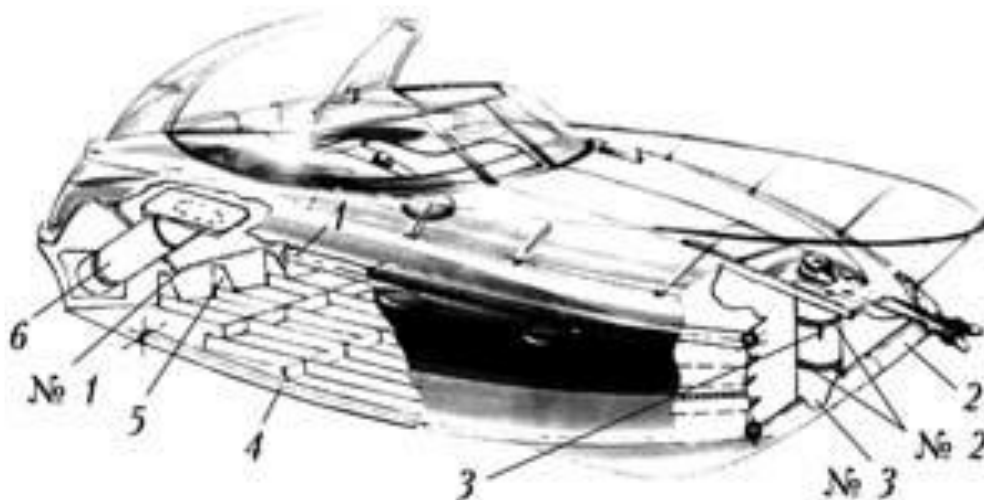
Схема выполнения сварных соединений на корпусе катера
